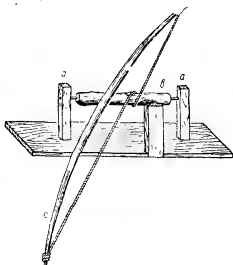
Токарный станок с ручным лучковым приводом. Реконструкция проф. Фельдхауза.
